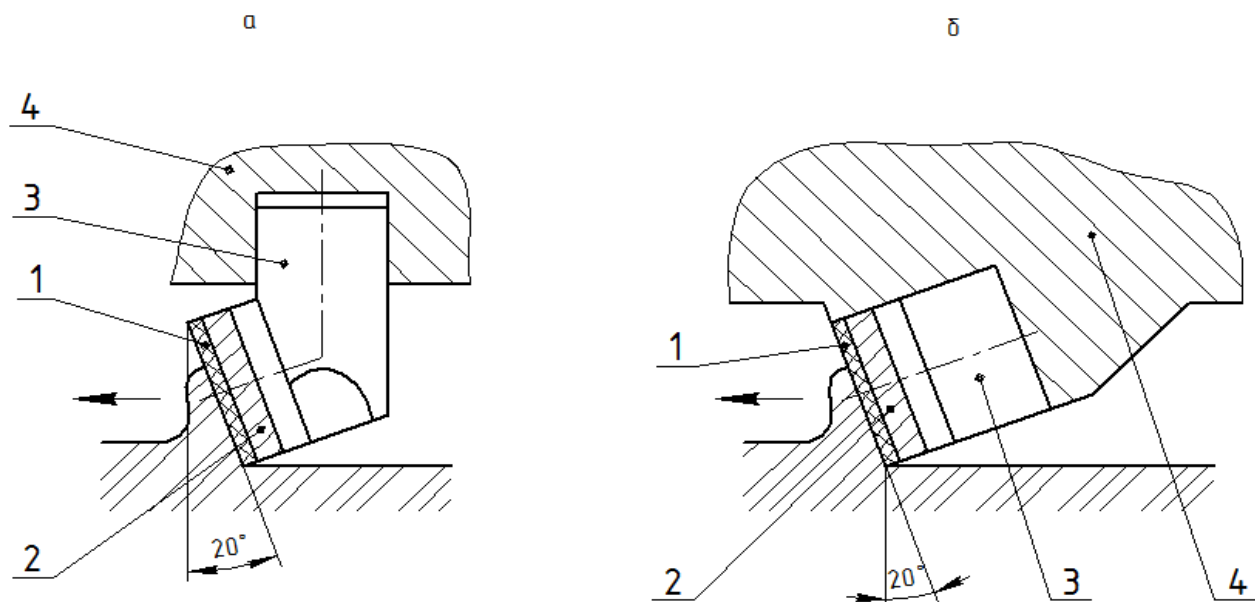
Крепление алмазно-твердосплавной пластинки
